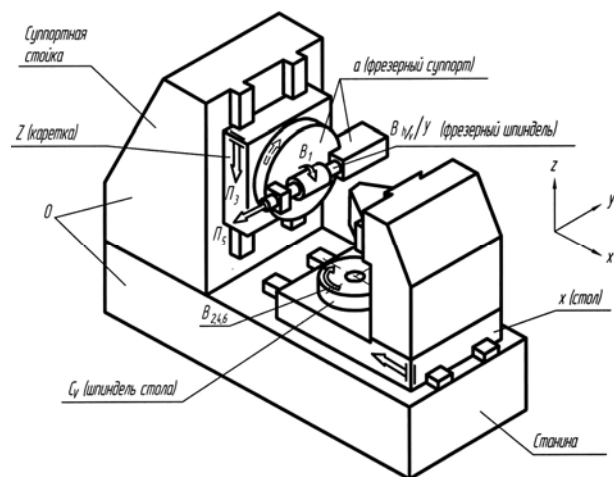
Компоновка зубофрезерного станка типа ВК1
